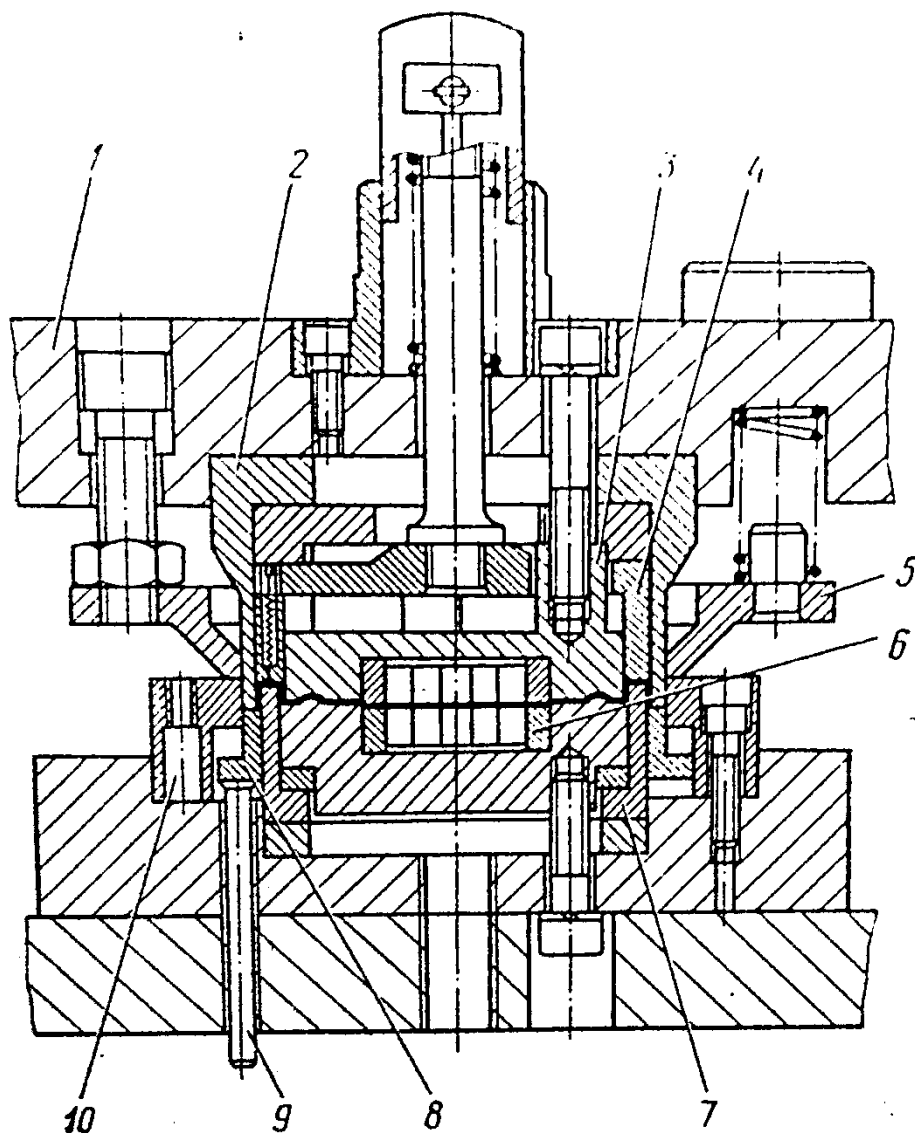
Комбінований штамп для виготовлення кришок
